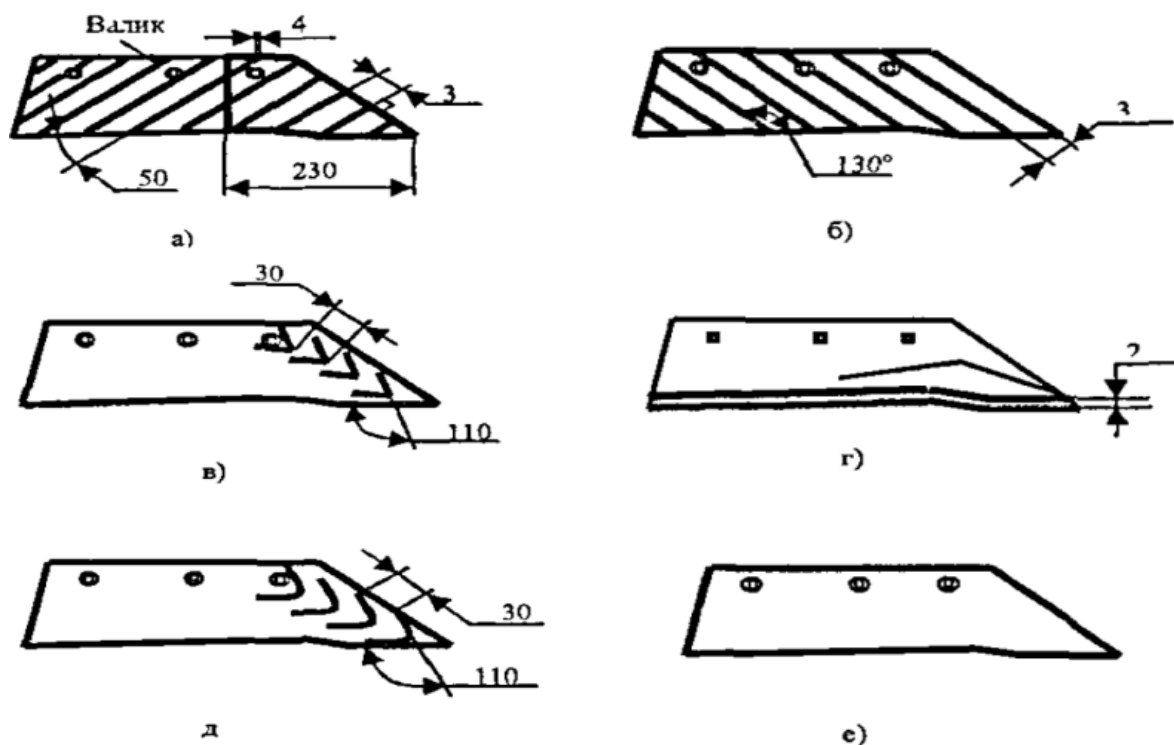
Схеми наплавлення валиків на поверхню леміша
